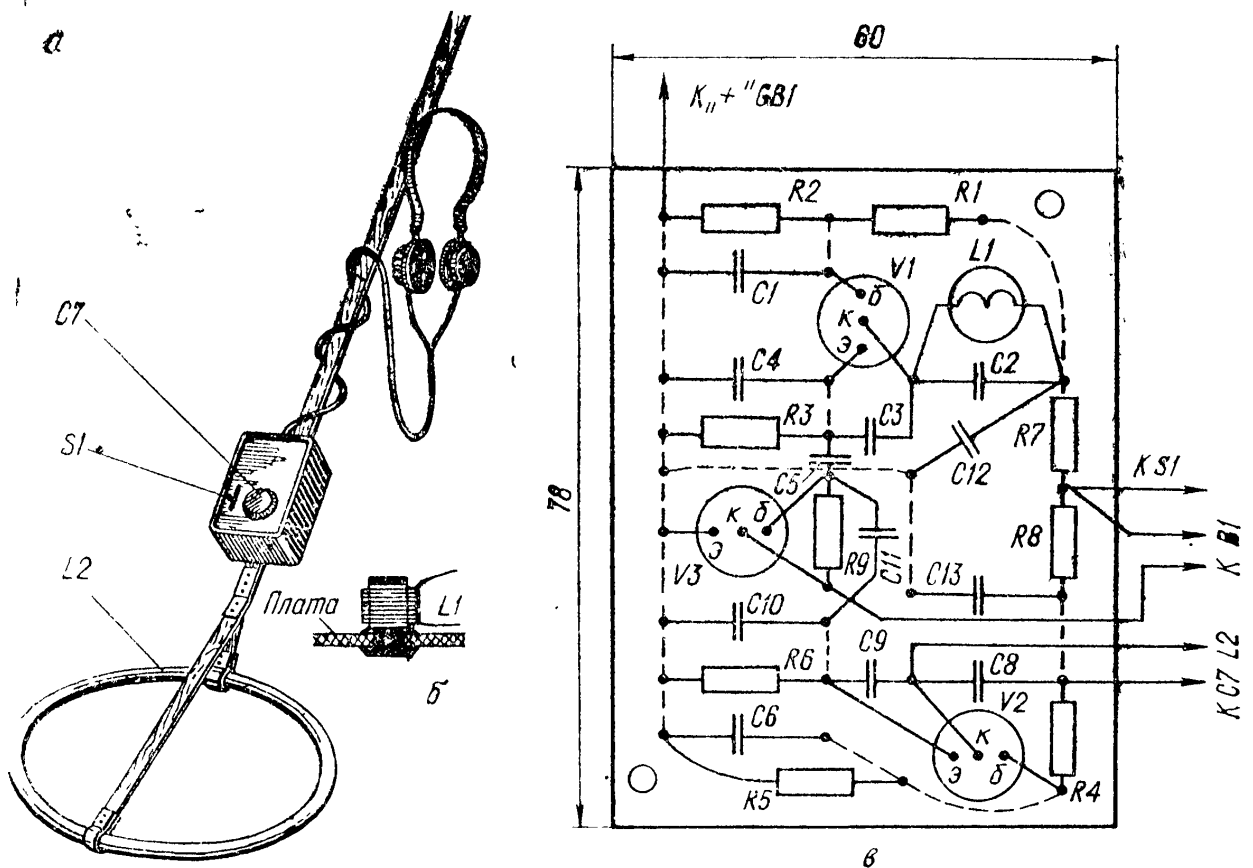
Внешний вид (а), контурная катушка (б) и схема соединения деталей (в) миноискателя
